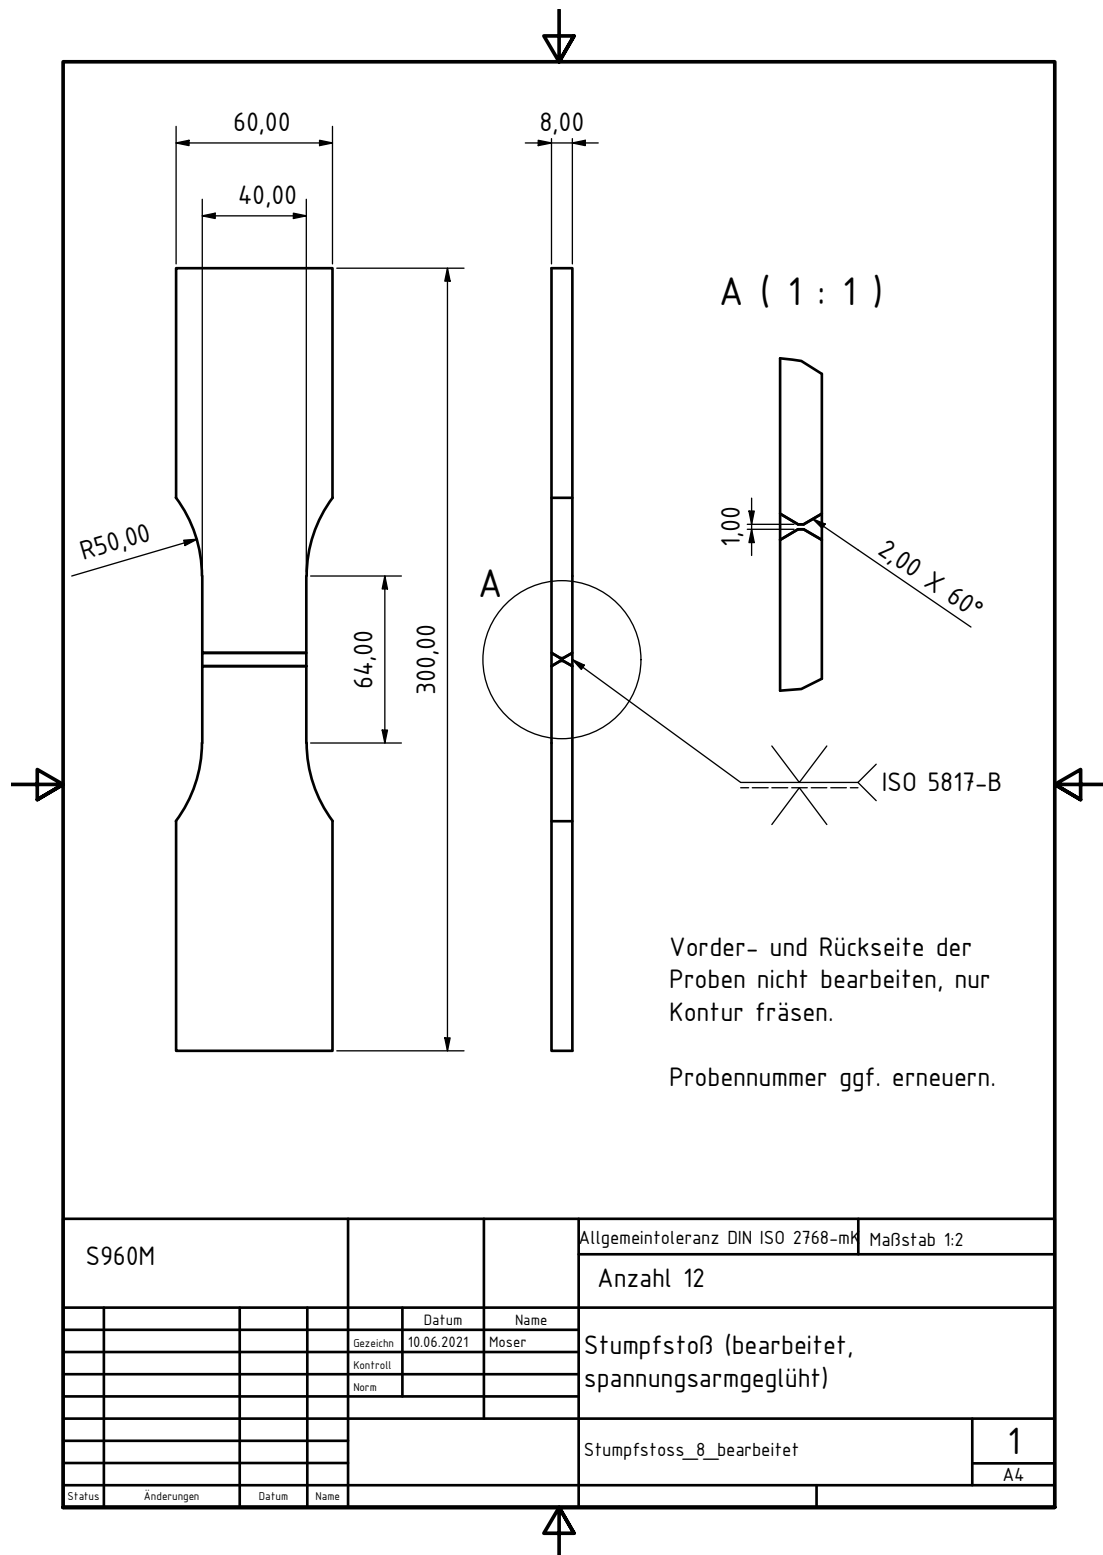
Fertigungszeichnung für die Stumpfstoßproben aus S960M.
